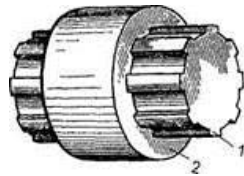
Зубчатое (шлицевое) соединение: 1 — вал; 2 — ступица колеса
